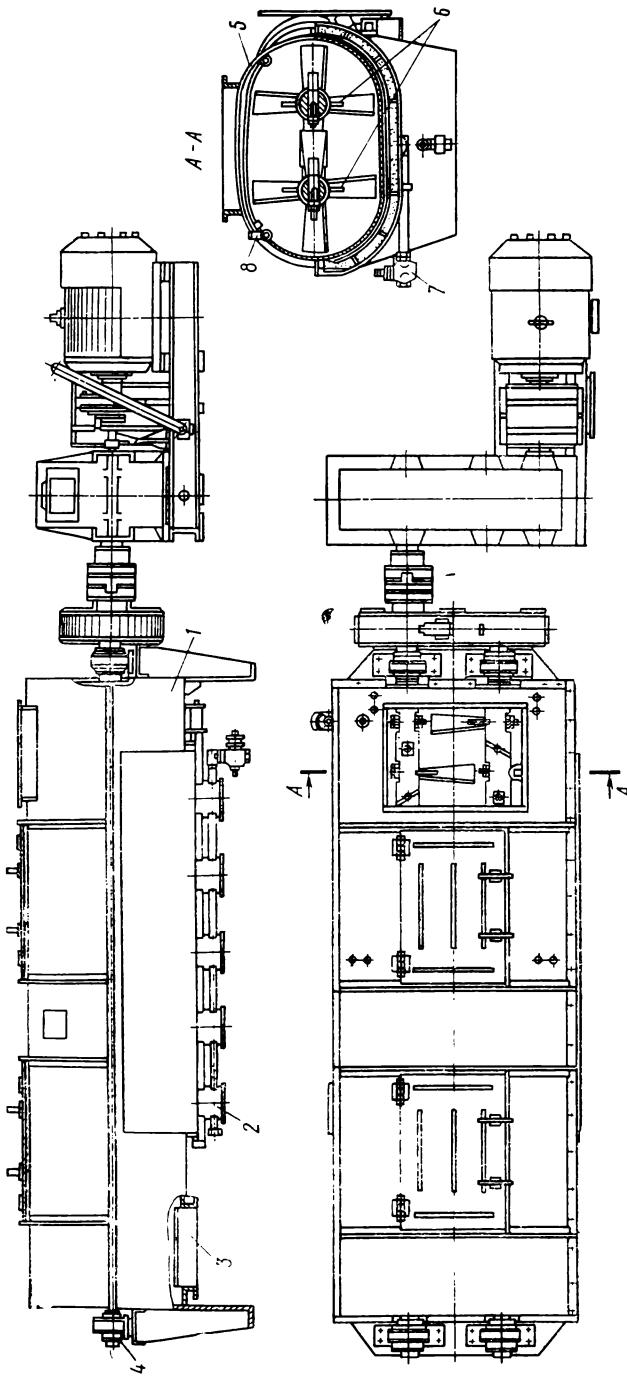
Лопастный двухвальный смеситель СМК-126:
